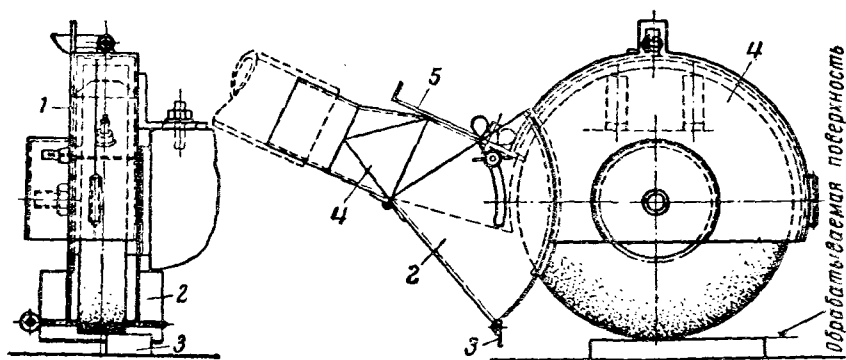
Конструкция кожуха для плоскошлифовального станка
